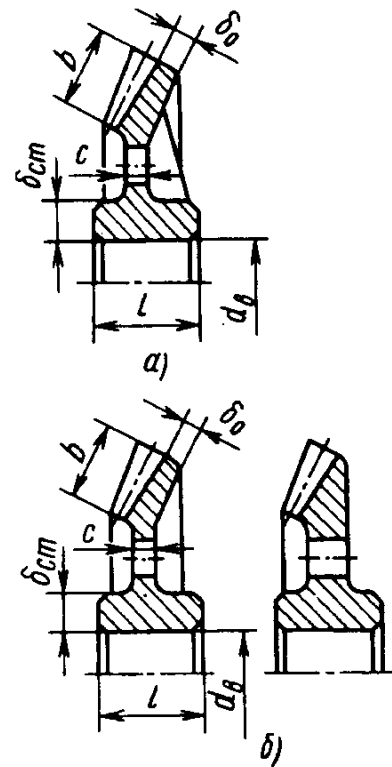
Конструкции конических колес: а - литых; б - кованых
